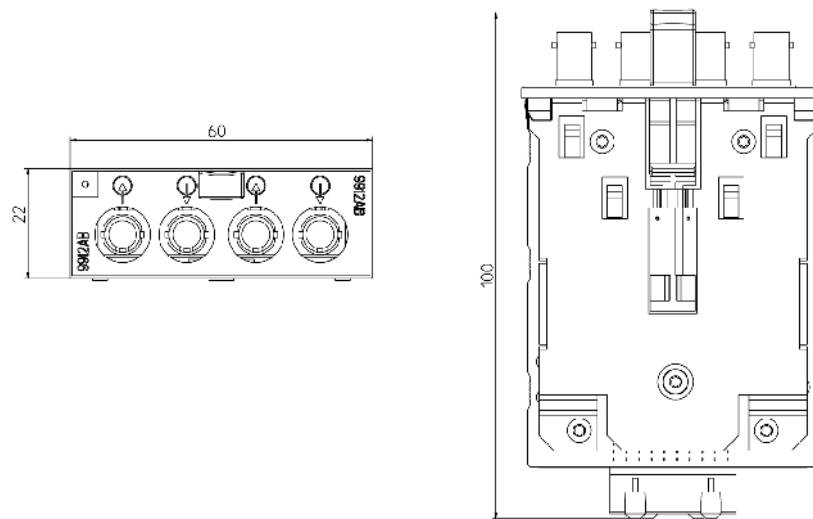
MM900 Dessin coté 3 : Ports BFOC
